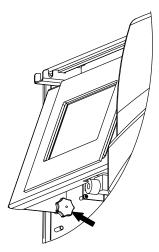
Position der Schrauben der Touchscreen-Baugruppe
